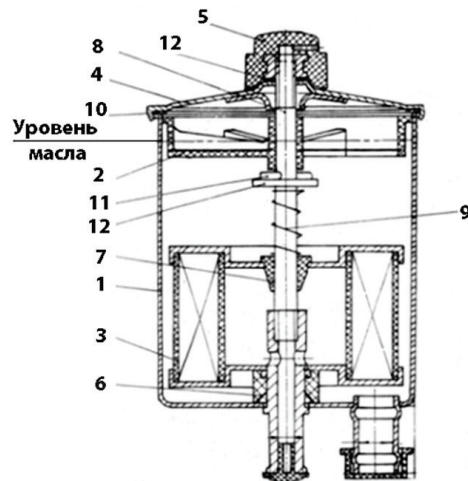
Бачок ШНКФ 453473.300 усилителя рулевого управления: 1 – корпус; 2 - фильтр заливной; 3 – элемент фильтрующий; 4 – крышка; 5 - пробка; 6 – вставка; 7 – шайба фильтра; 8 – шпилька; 9 – пружина клапана; 10 - прокладка уплотнительная; 11 – шплинт; 12 – шайба.
